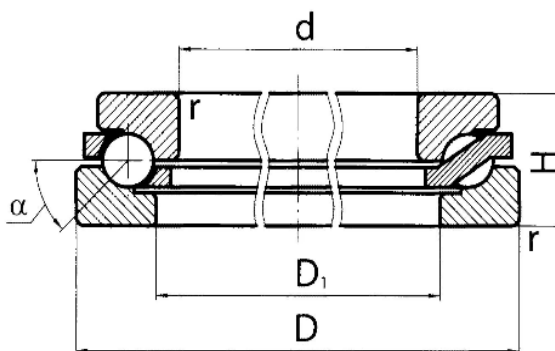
Упорно-радиальный шариковый подшипник
